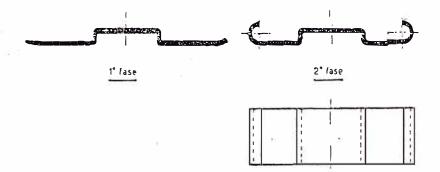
Fases de doblado realizables con una sola estampa
